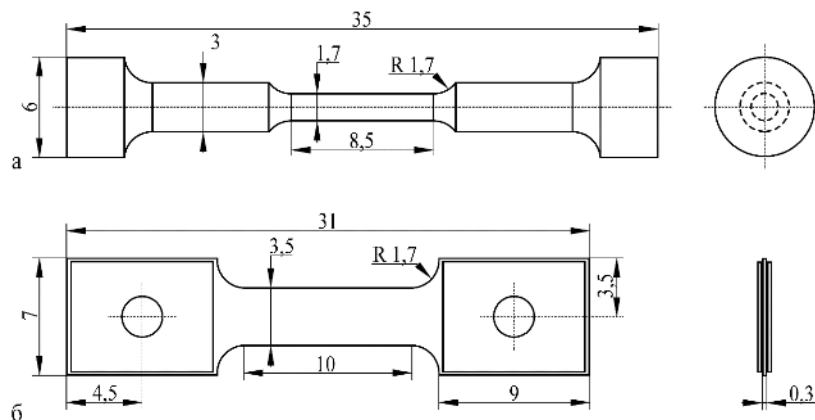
Образцы на растяжение: а — цилиндрический, б — плоский в форме двойной лопатки. Размеры указаны в мм
